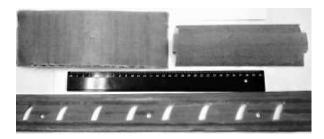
Внешний вид некоторых элементов конструкции решётки
